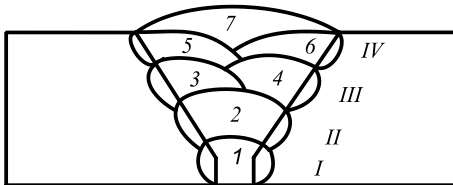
Многослойный сварной шов: *1–7* – последовательность выполнения переходов; *I–IV* – слои; *1* – корневой шов; *7* – облицовочный шов
